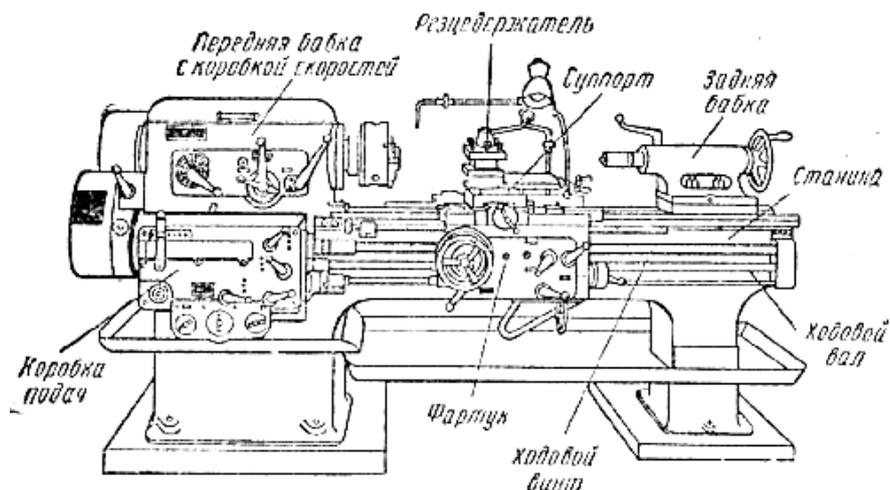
Токарно-винторезный станок с коробкой скоростей.
